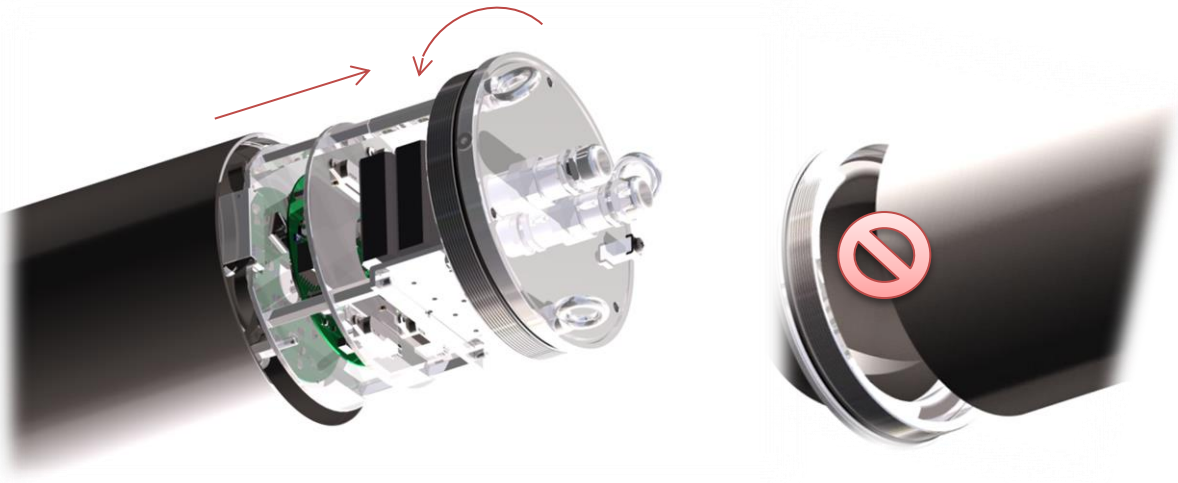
Abertura do flange de tampa de tipo T08-TNXCD
